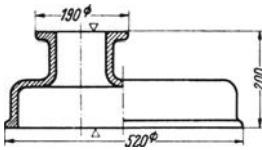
Deckel mit Stützen (Werkzeichnung).
